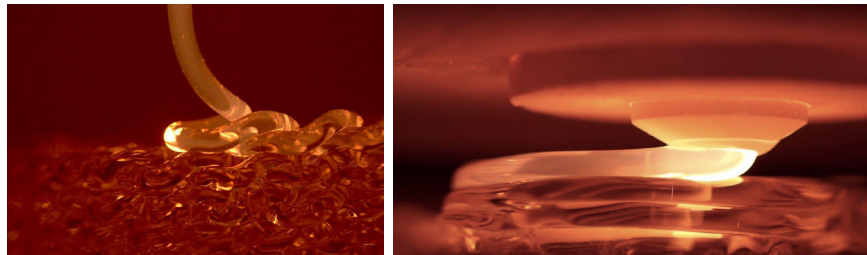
Vista detallada de las primeras pruebas de impresión 3D de vidrio
